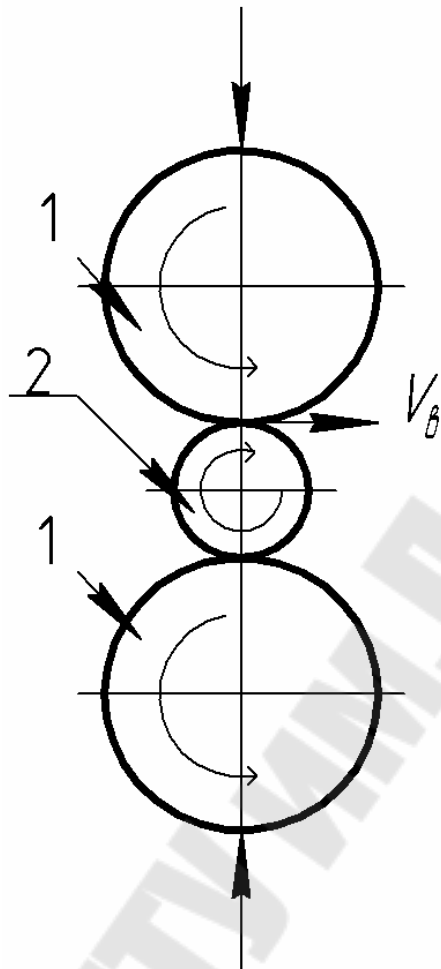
Схема поперечной прокатки: 1 – прокатные валки; 2 – заготовка
